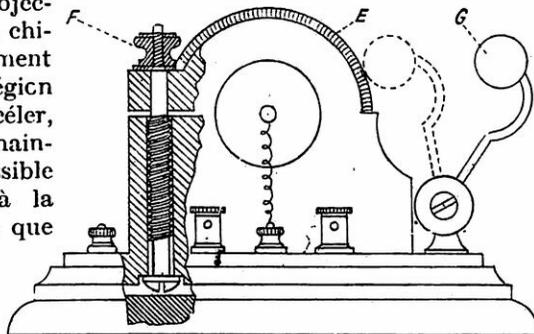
VUE EN BOUT DU GROUPE FIXE
